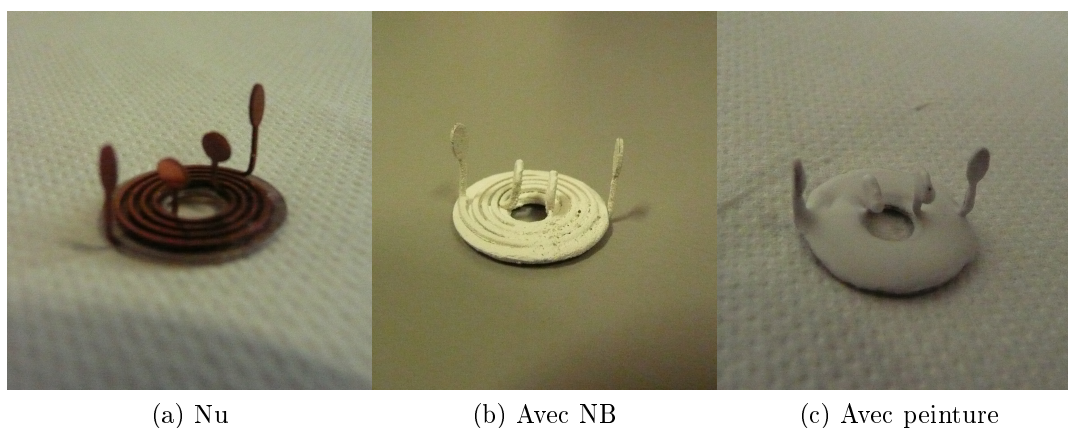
Assemblage rondelles-spirales recouvert.
